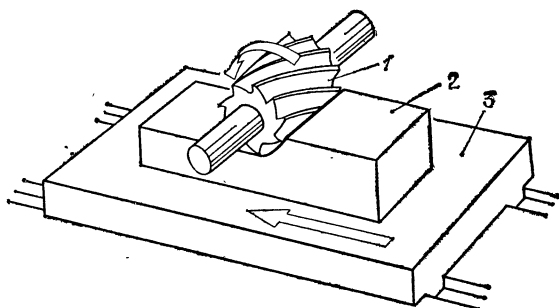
Фрезерование: 1 — вращающаяся фреза, 2 — обрабатываемая металлическая заготовка, 3 — подвижный стол.
